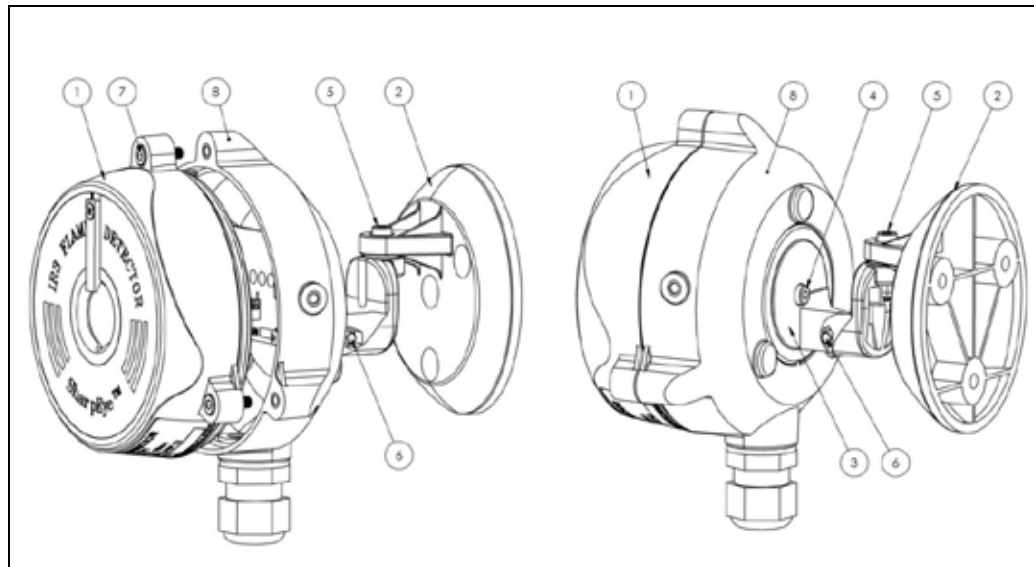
Montage von IR3-Melder und Schwenkhalterung
